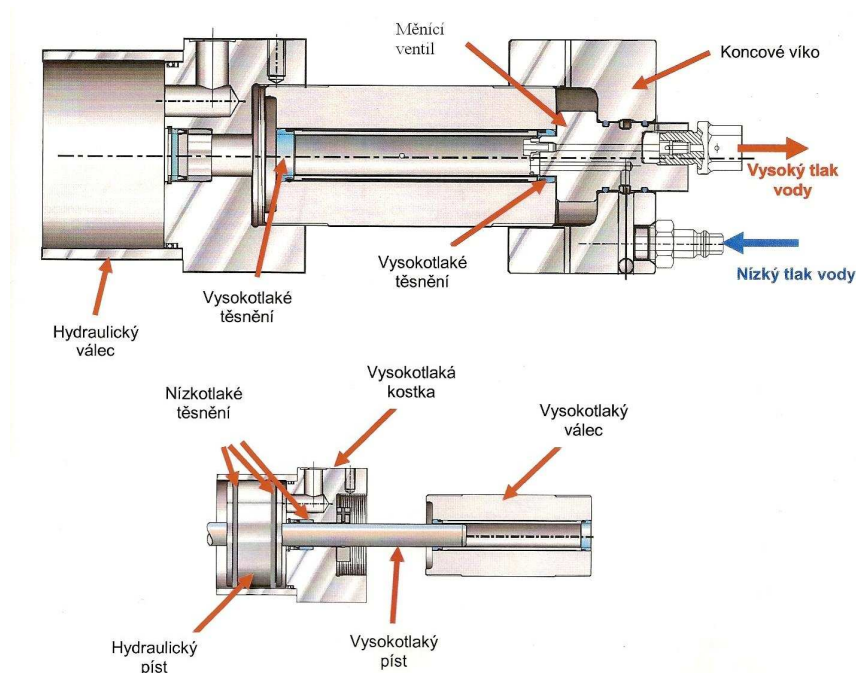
Multiplikátor 60K - technické řešení – [7]
